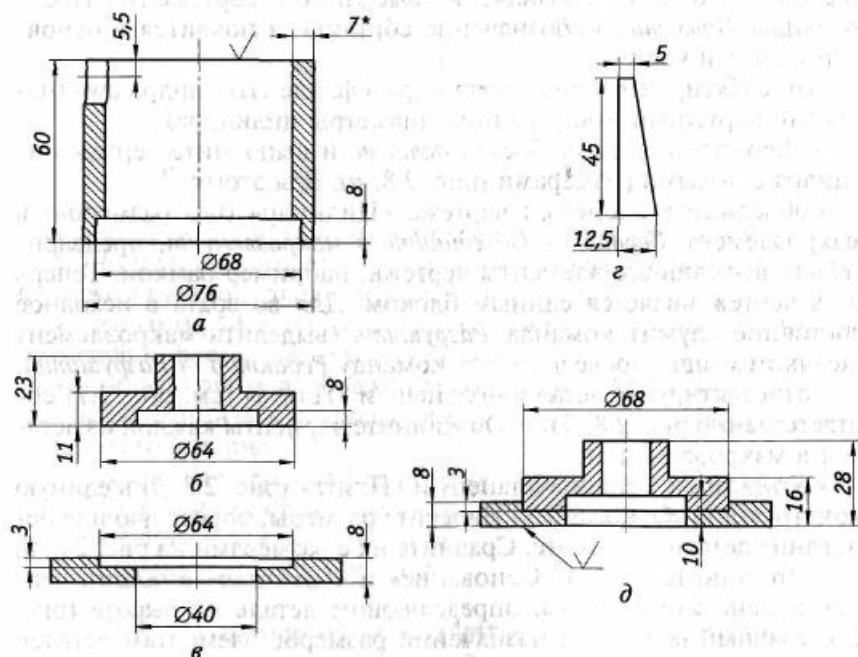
Компоненты сборочной единицы «Корпус сварной»:
